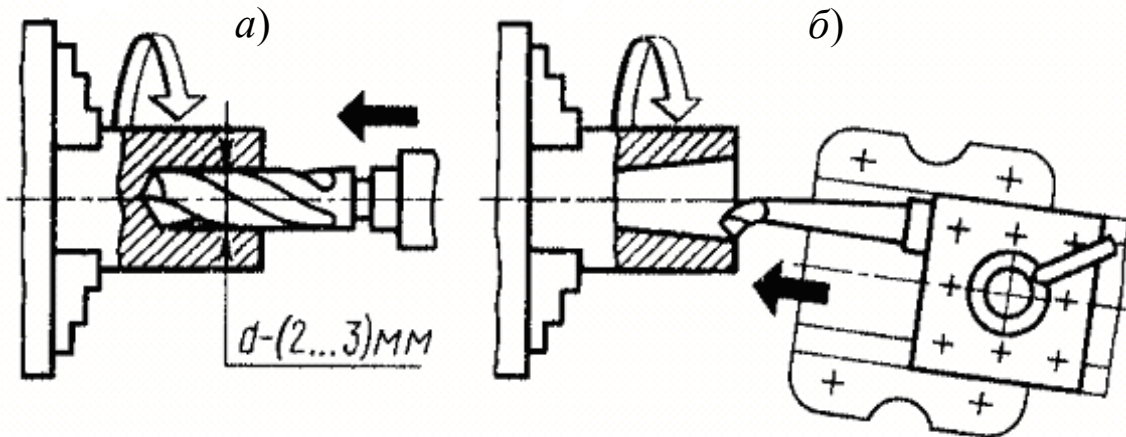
Обработка внутренней конической поверхности способом поворота верхней части суппорта:
